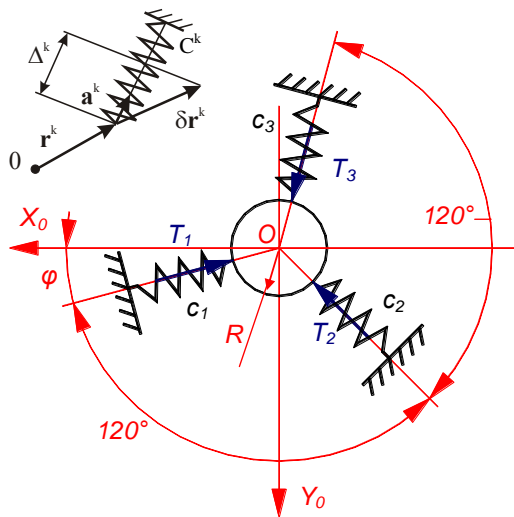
Розрахункова схема пружної системи патрон-заготовка в поперечному перетині при дворізцевій обробці
